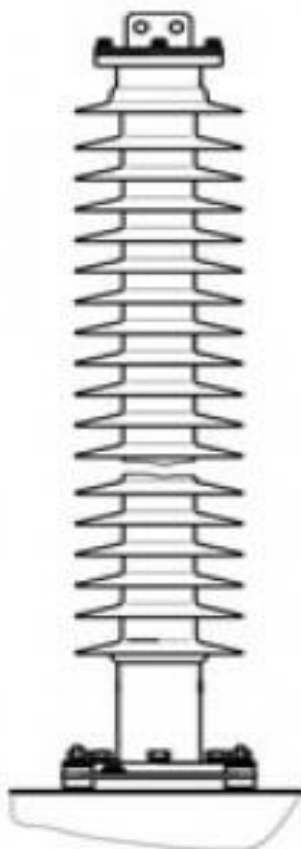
Внешний вид ОПН-П1-110/88/10/2УХЛ1
